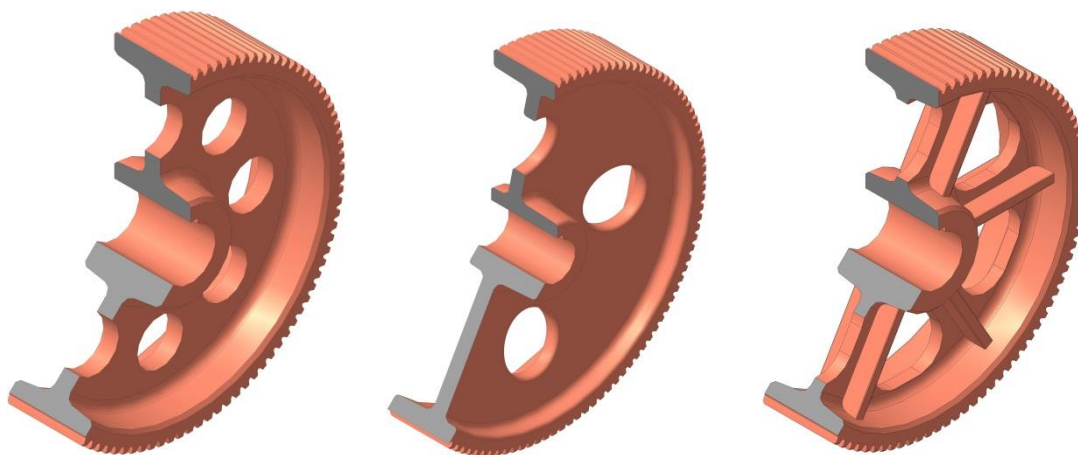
Зубчасті колеса виготовлені за допомогою литва
